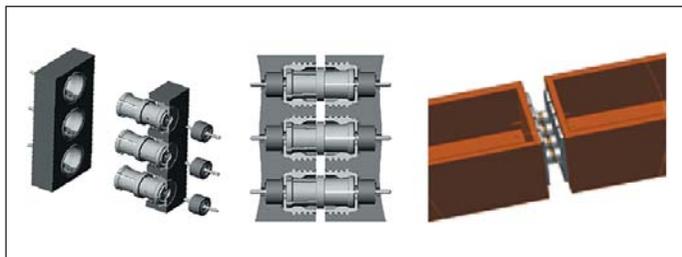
SMP-соединители в СВЧ-модулях [5]
